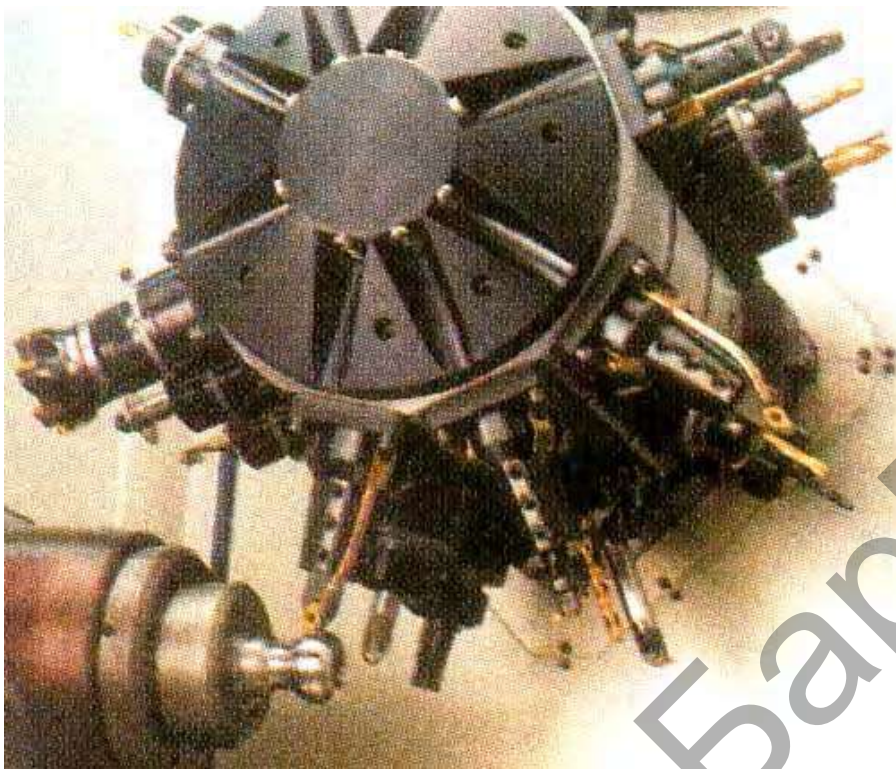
Револьверная головка на 24 инструмента из которых
